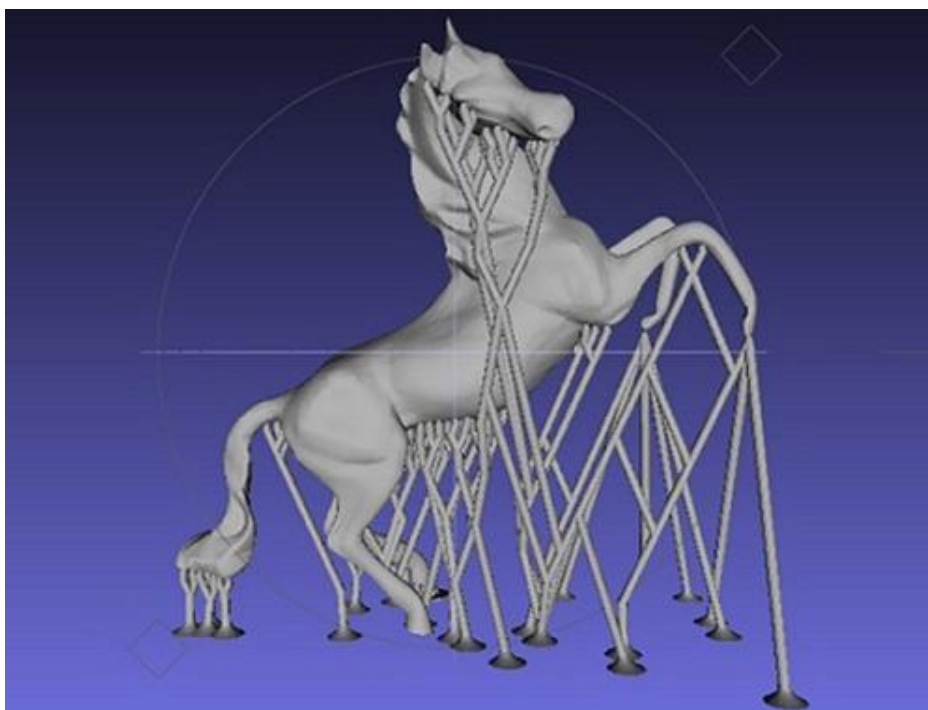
Цифровая модель с поддерживающими конструкциями
